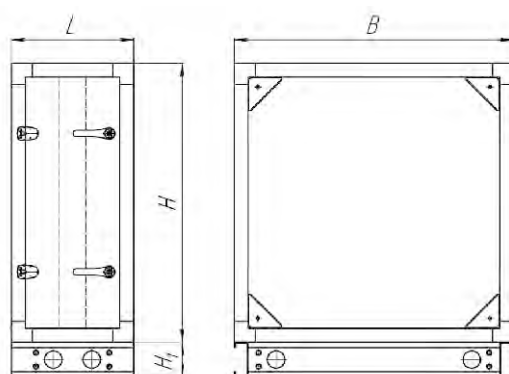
Габаритные и присоединительные размеры. Блок ячеякового фильтра.
